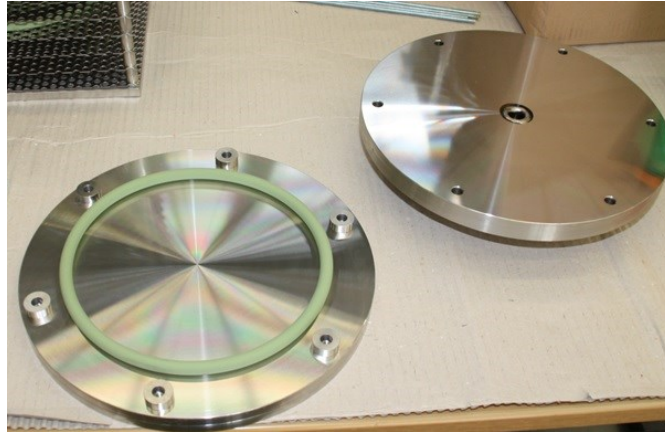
rundes Flanschpaar für Druckanstiegsmessung/Dichtheitsprüfung mit FKM-O-Ring
